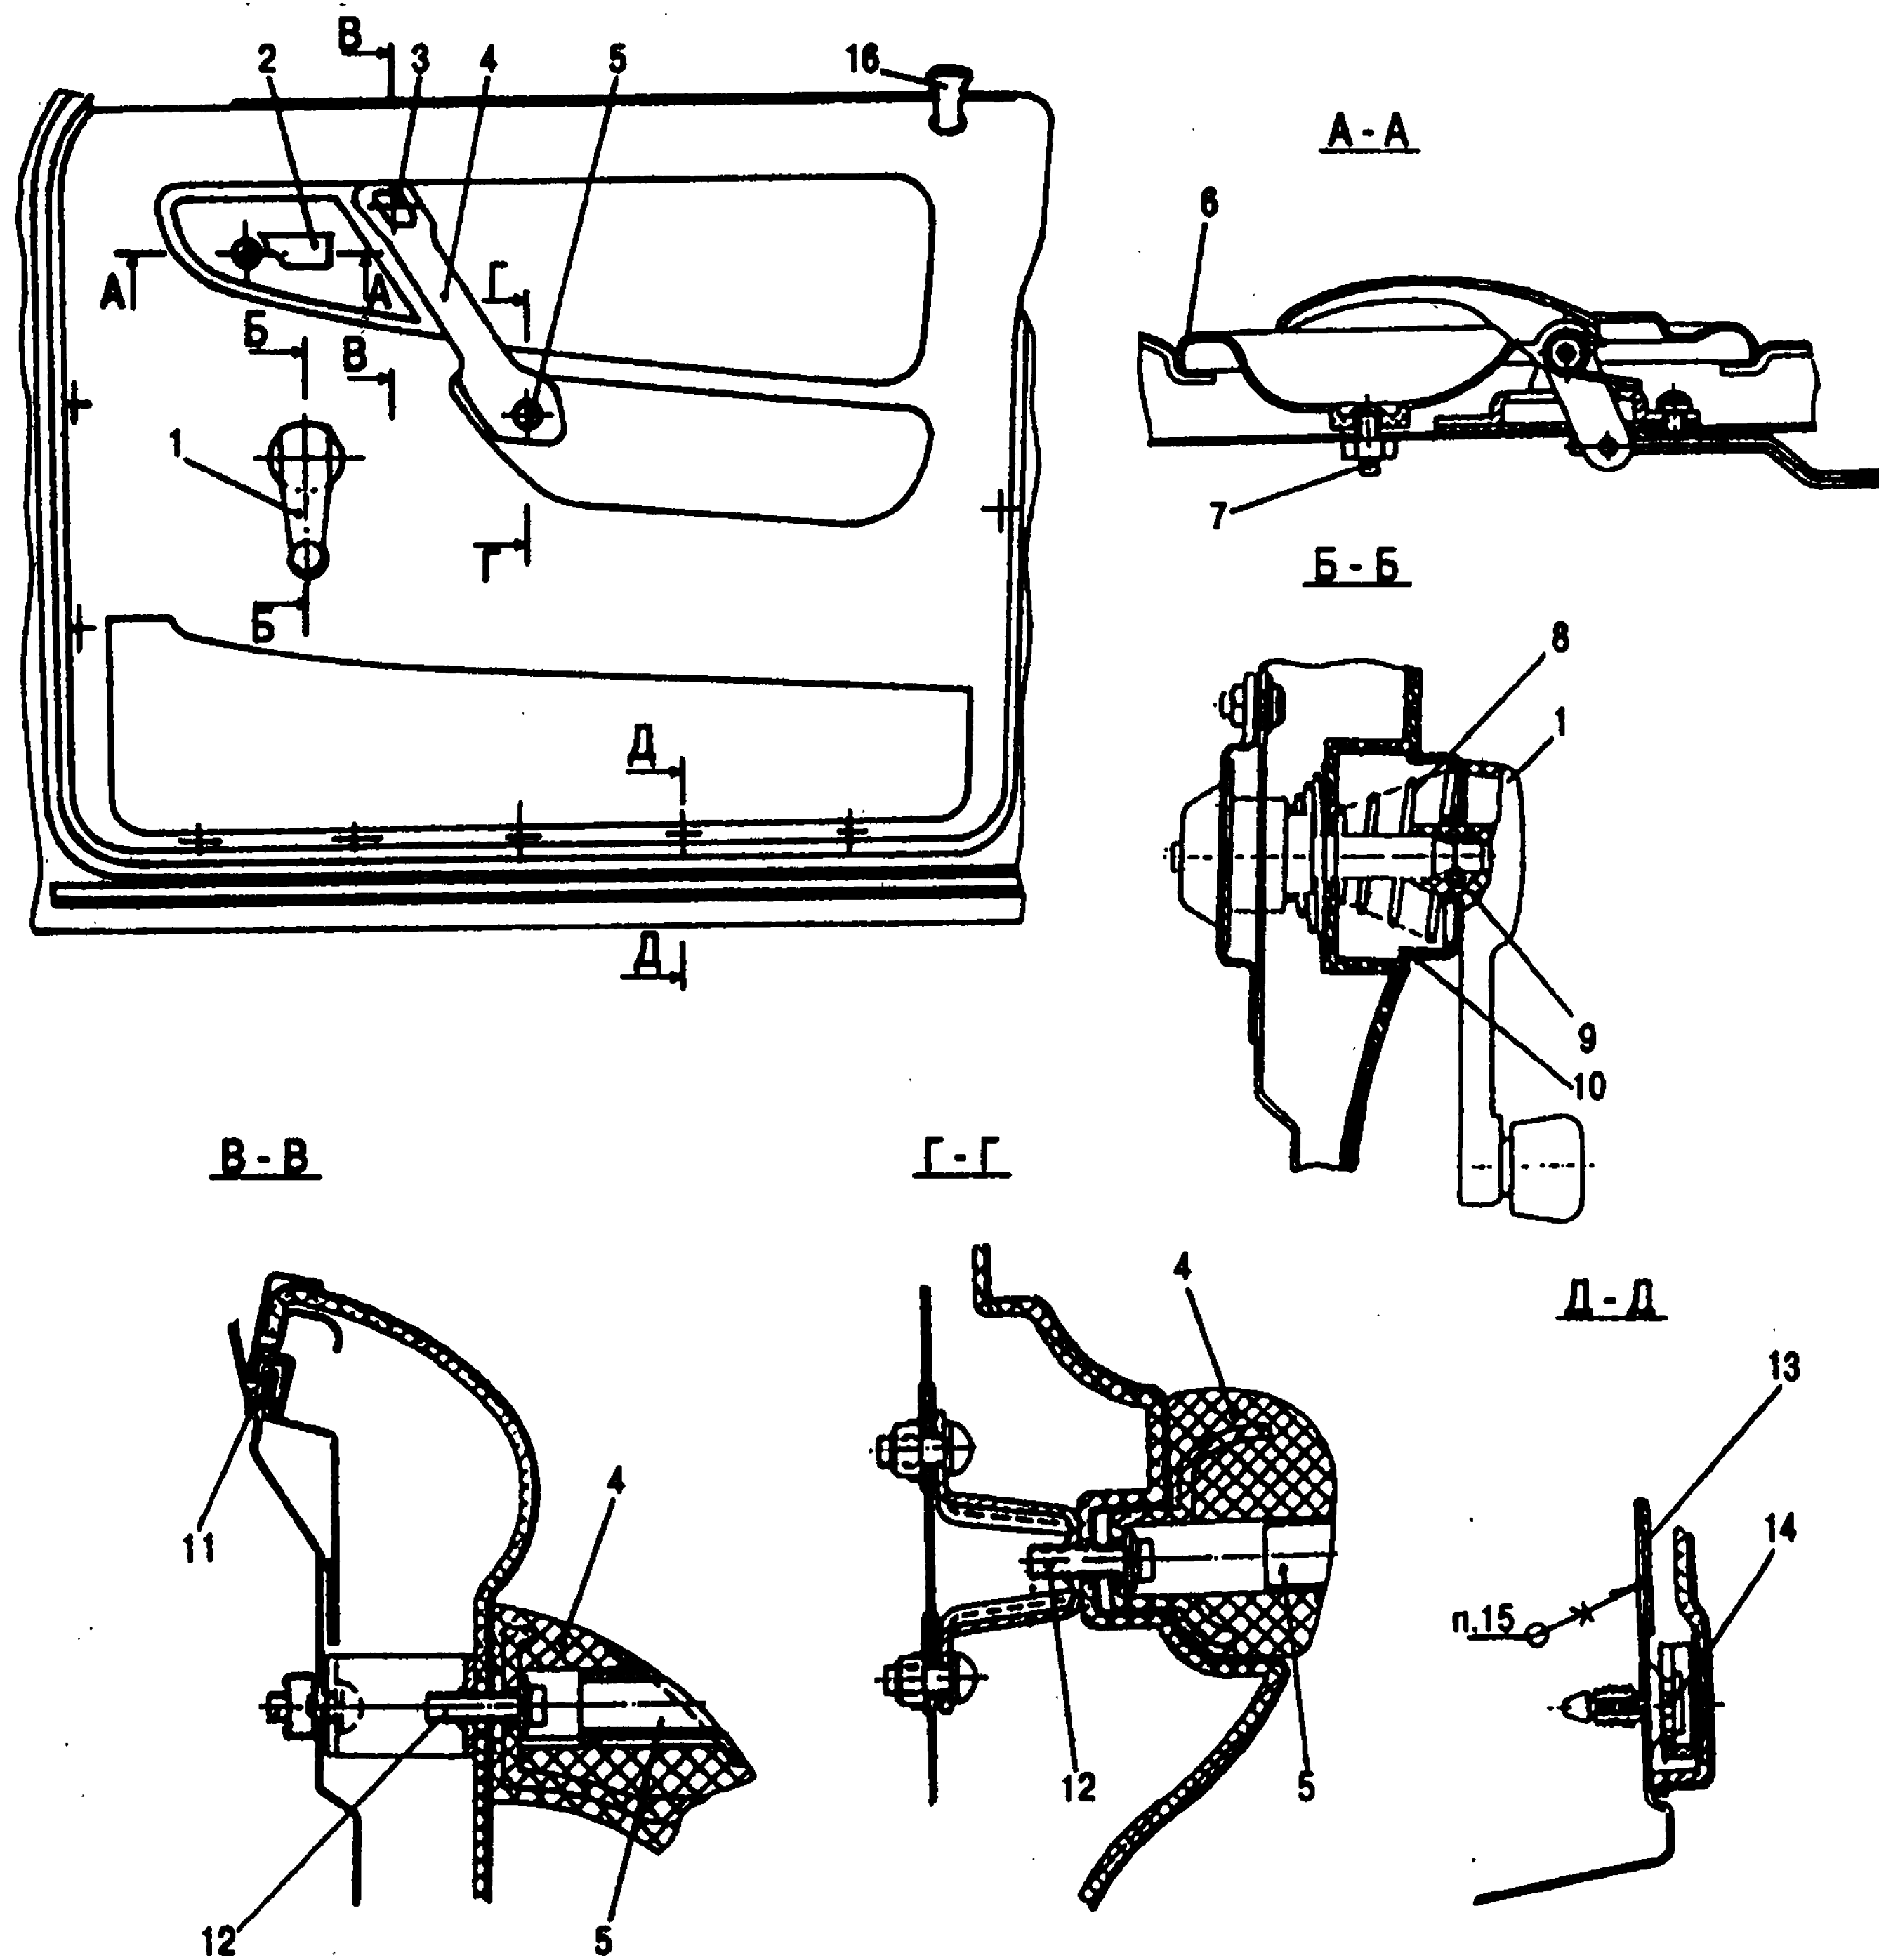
Обивка двери (передняя правая): 1 - ручка стеклоподъёмника; 2 - привод замка внутренний; 3 - пробка верхняя; 4 - ручка подлокотника; 5 - пробка нижняя; 6 - розетка внутреннего привода; 7 - винт М6 крепления розетки; 8 - пружина; 9 - штифт; 10 - розетка ручки; 11 - уплотнитель опускающего стекла; 12 - болт СП М6х16; 13 - прокладка уплотнительная; 14 - пистон; 15 - клей для прокладки; 16 - кнопка тяги выключения замка
